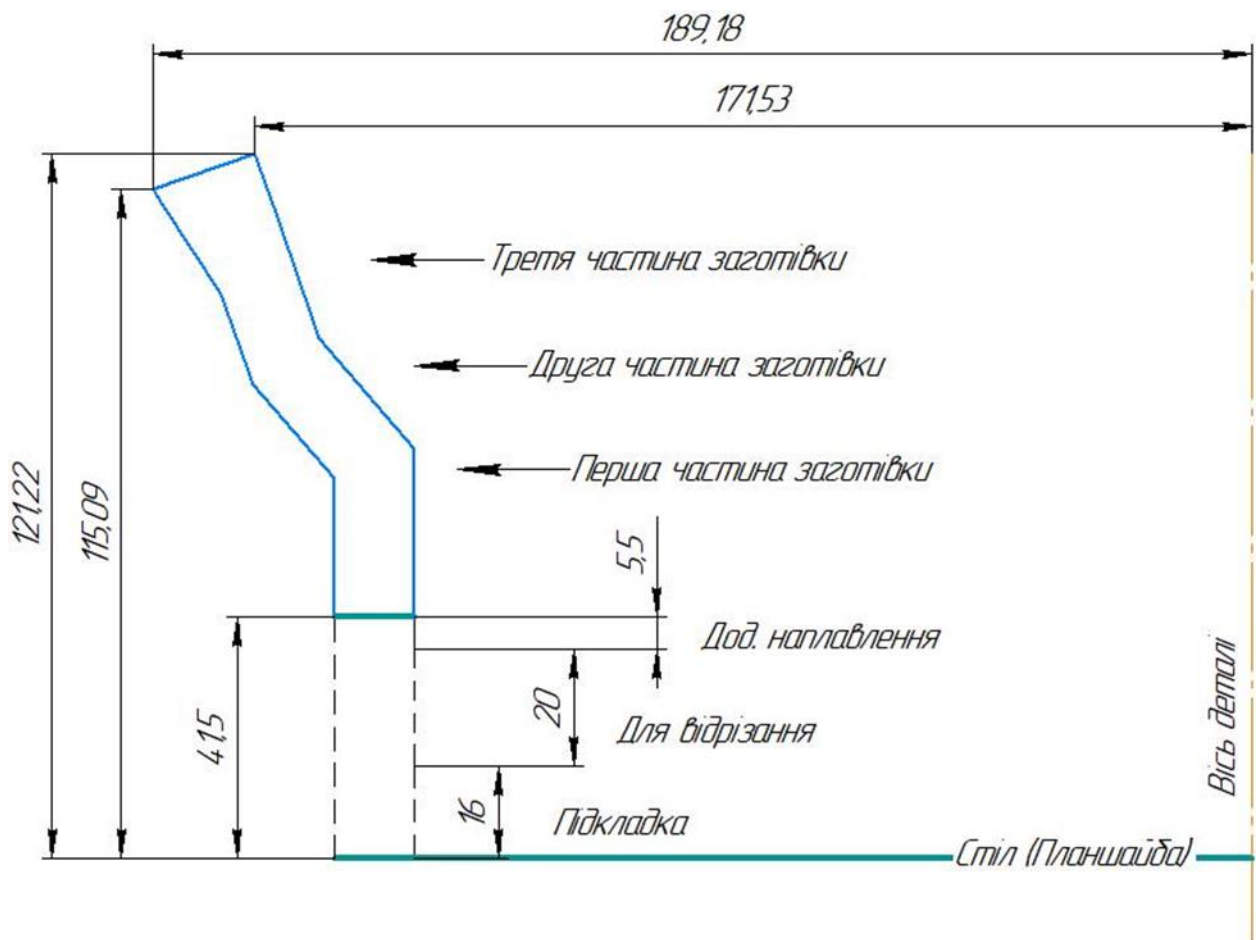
Креслення третьої частини заготівлі 4500301001 (Зроблено в КОМПАС-3D v17)
